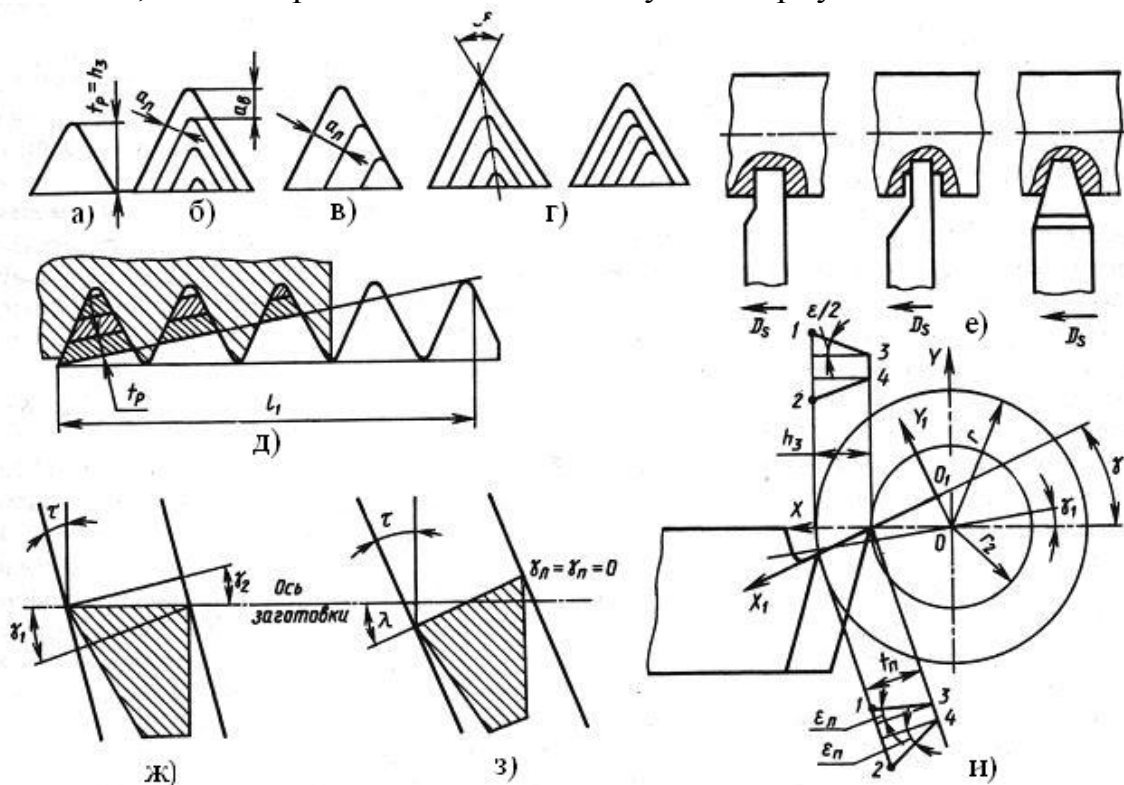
Схемы нарезания и геометрия резбовых резцов
